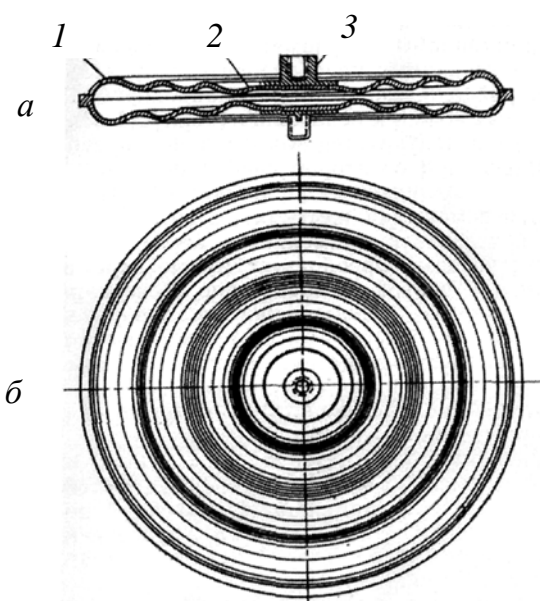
Барокоробка: *а* – разрез; *б* – вид сверху;
